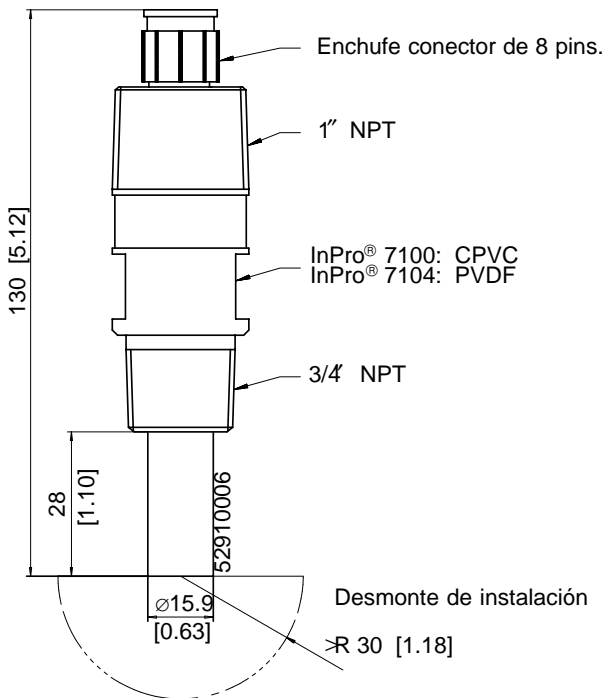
Esquema de dimensiones de InPro®7100/7104 de célula de 4 electrodos
